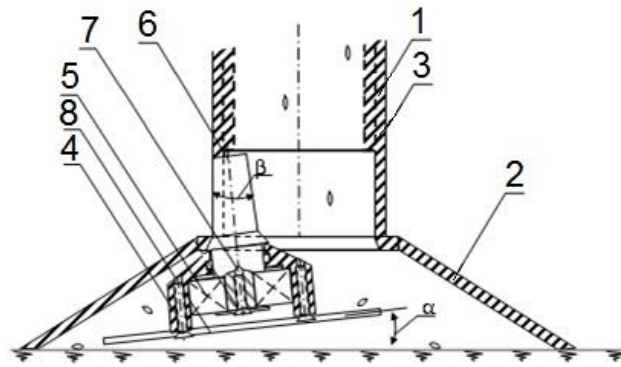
Конструктивна схема сошника з роликом-розсіювачем:
